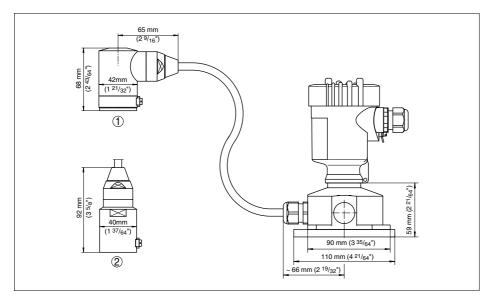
IP 68-Ausführung mit externem Gehäuse - Nicht-Ex
